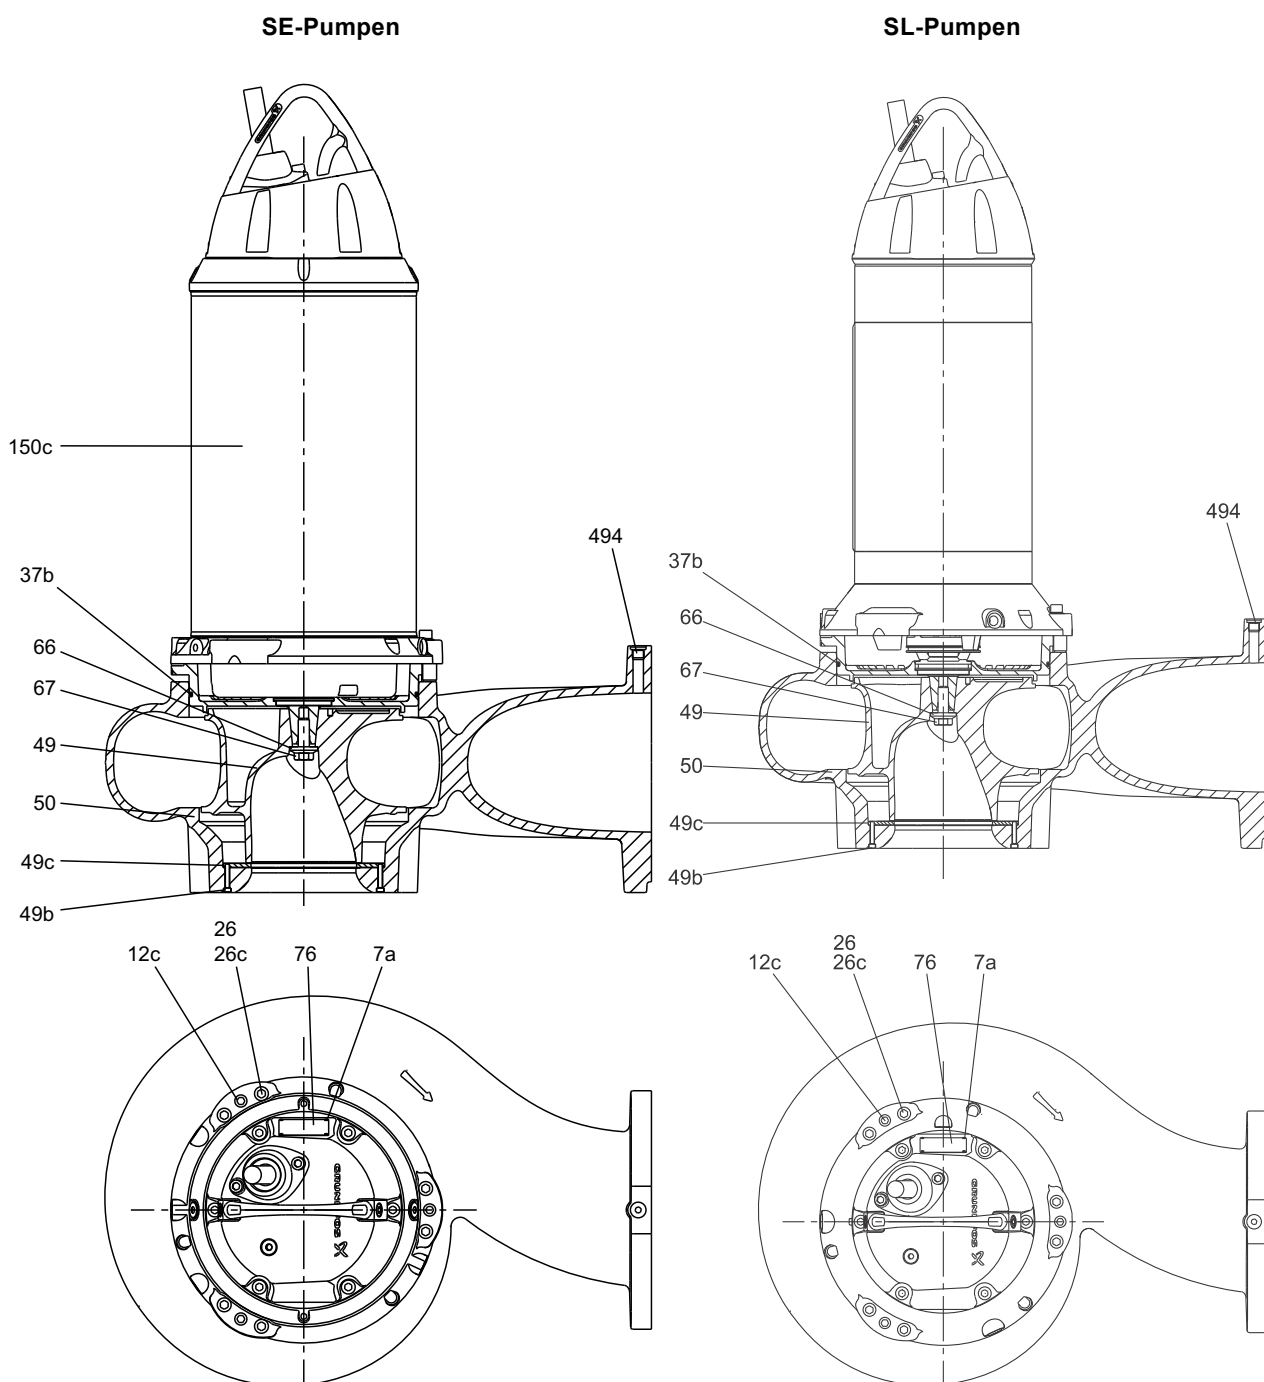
SE- und SL-Pumpen mit S-tube®-Lauf­rad
